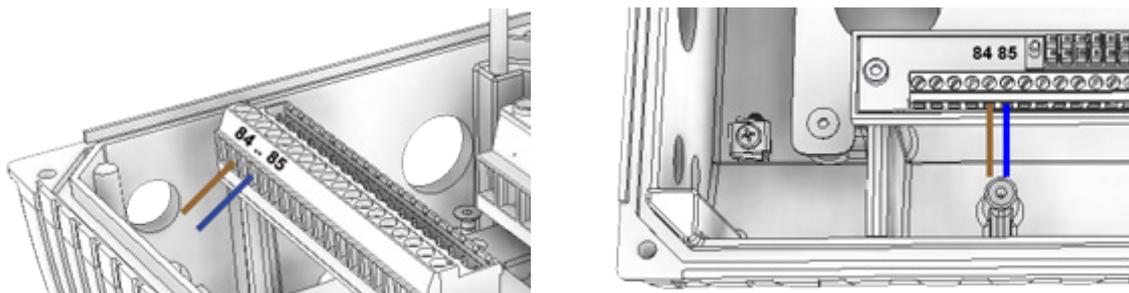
Клеммы подключения AS-i, слева — типоразмеры 1 – 3, справа — типоразмер 4
